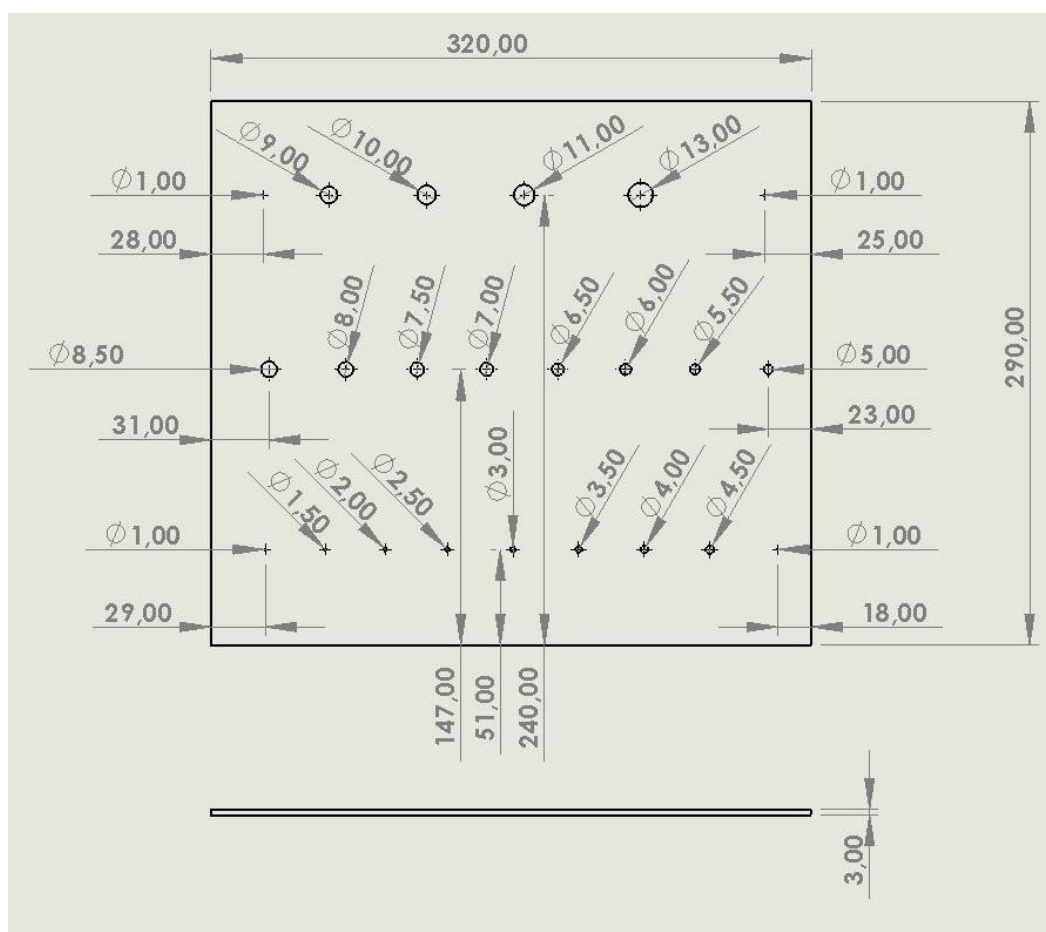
Desenho técnico 2D relativo ao laminado constituído por furos não passantes (dimensões em mm).
